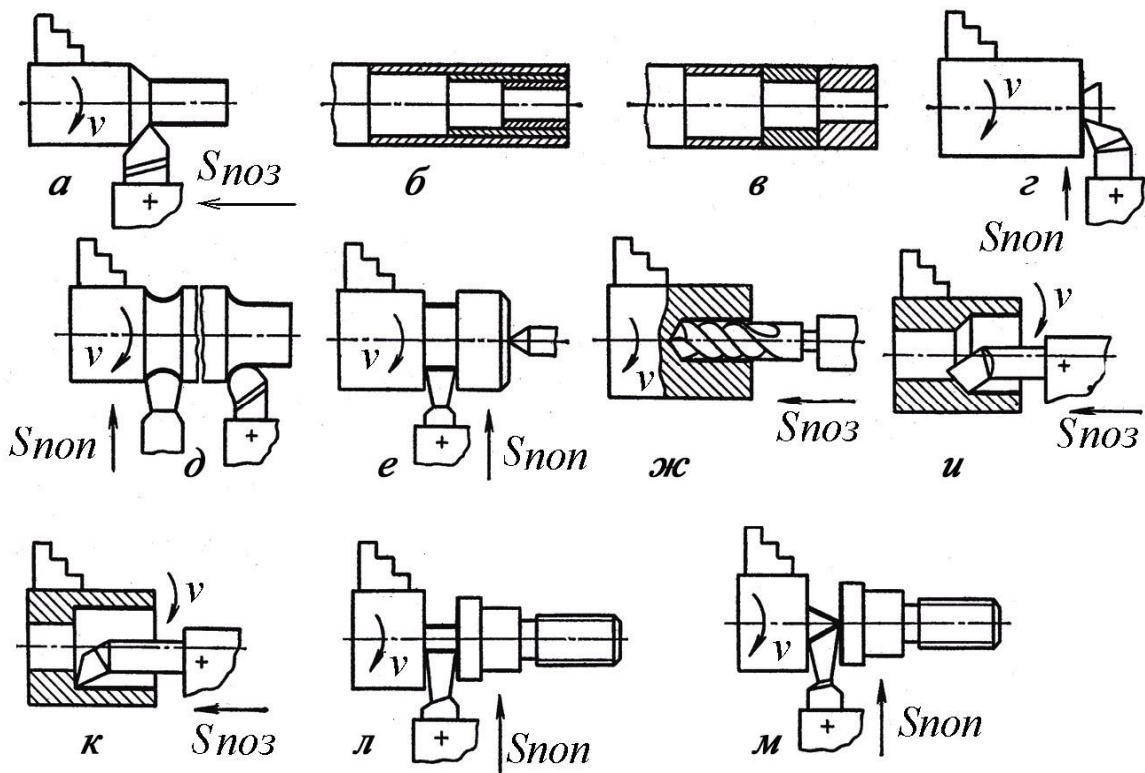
Схеми обробки заготовок на токарних верстатах
